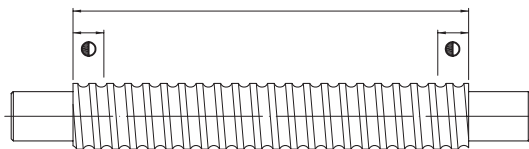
Bereich der Oberflächenhärtung einer Kugelgewindespindel
